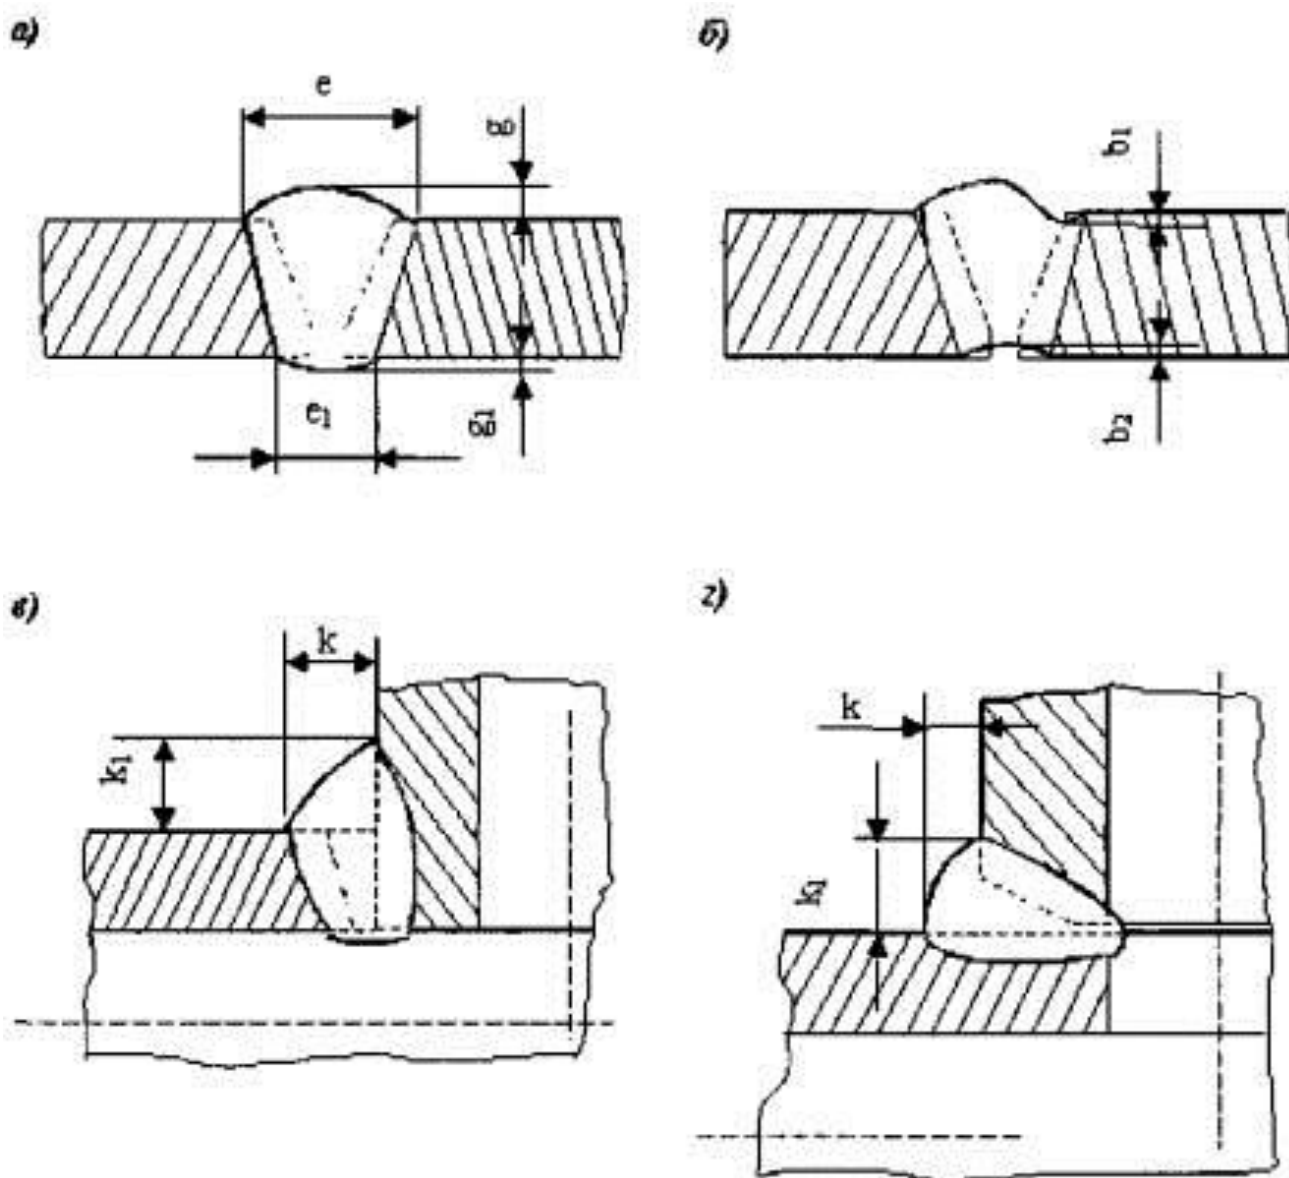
Параметры сварных швов стыковых и угловых соединений
